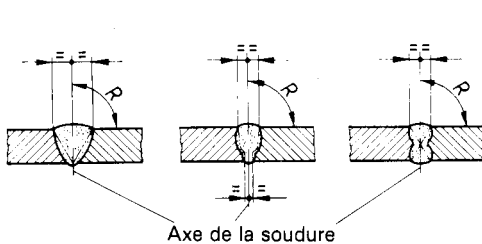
Exemples de rotation ($R = 90^\circ$) des soudures bout à bout symétriques sur surface de pièce horizontale
